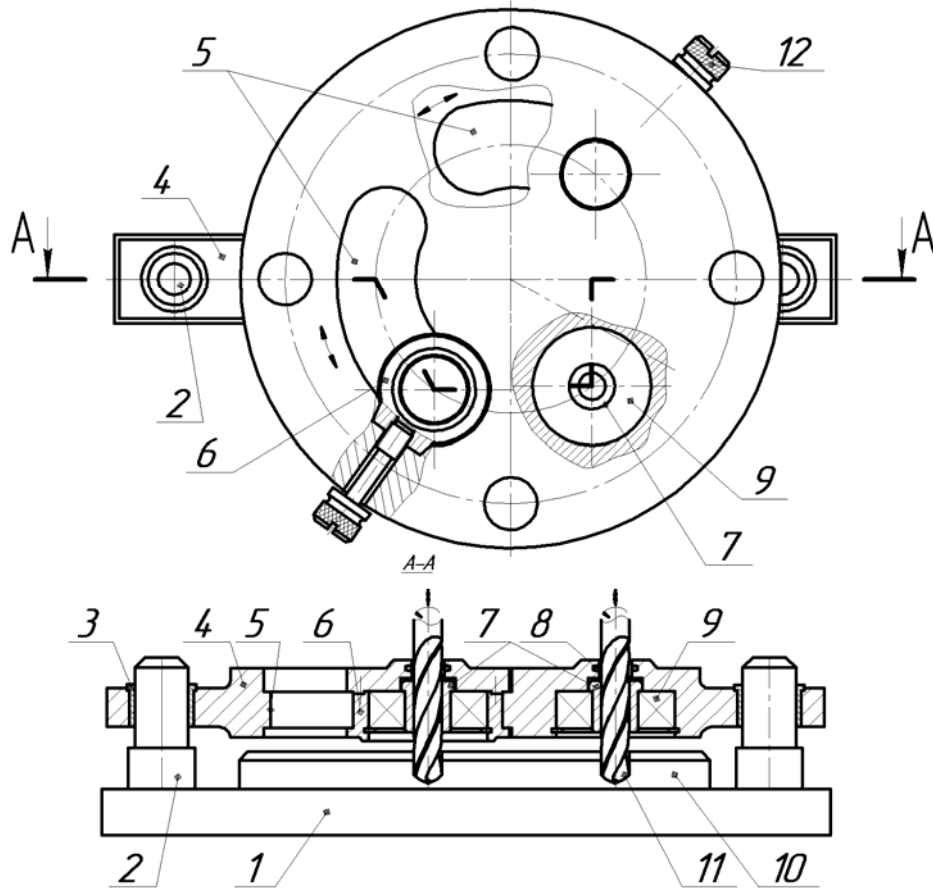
Переналагоджуваний кондуктор до багатошпindelьної свердлильної головки
